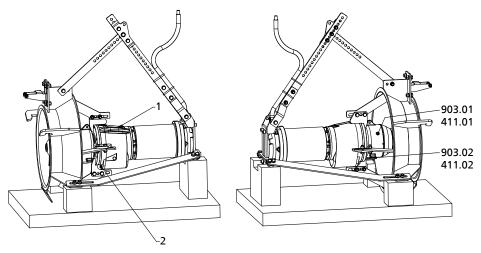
Drenaje del líquido lubricante; Amaline 500, 600, 800
